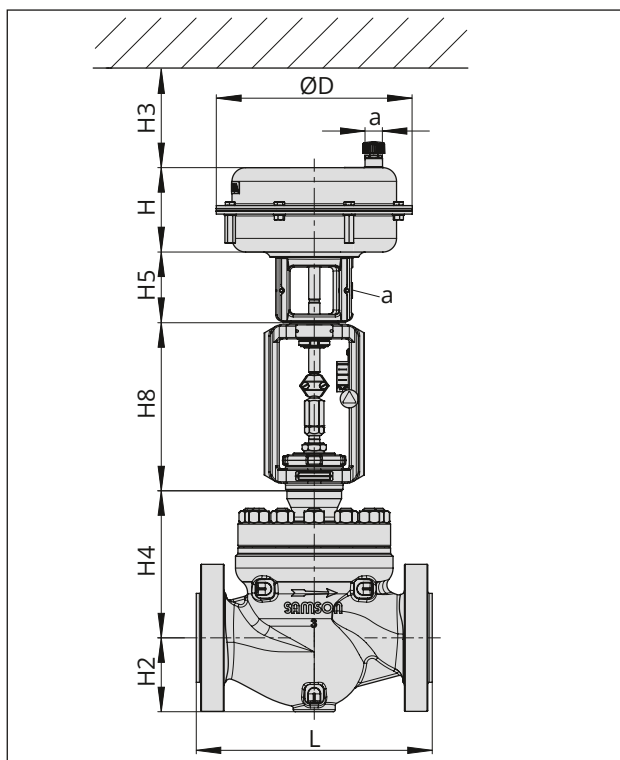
Регулирующий клапан SMS MG-7: клапан Тип 251GR с пневматическим приводом Тип 3277
